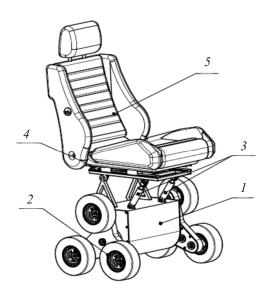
Конструкция СТС для перемещения по ступенчатым поверхностям: I — корпус с трансмиссией и приводами; 2 — колесный движитель; 3 — система адаптивной подвески; 4 — привод продольного перемещения; 5 — сиденье
